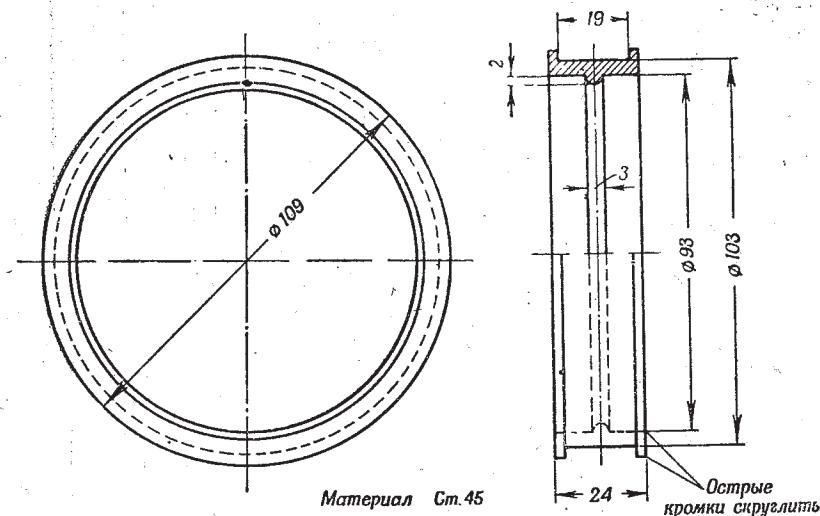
Размеры кольца для резинового амортизатора карданного вала мотоциклов М-72, М-75, М-76
